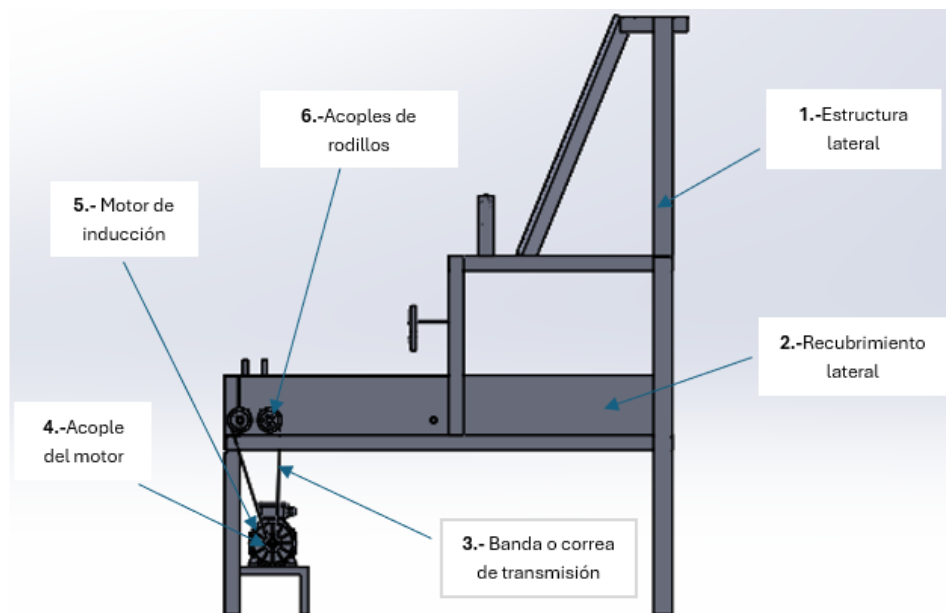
Alternativa 2. Sistema de distribución y estructura. Vista lateral.
